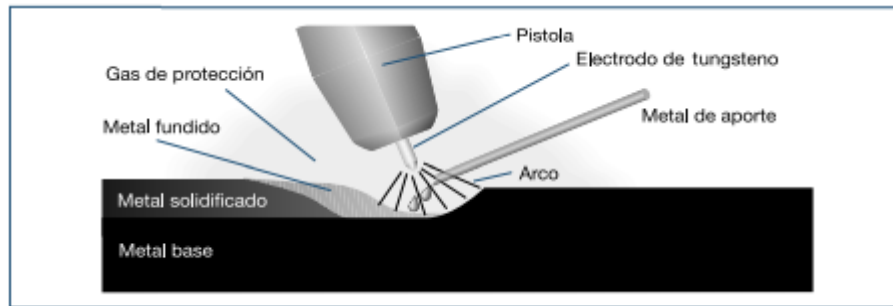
Soldadura con electrodo de tungsteno bajo la protección de gas (GTAW) [23].
